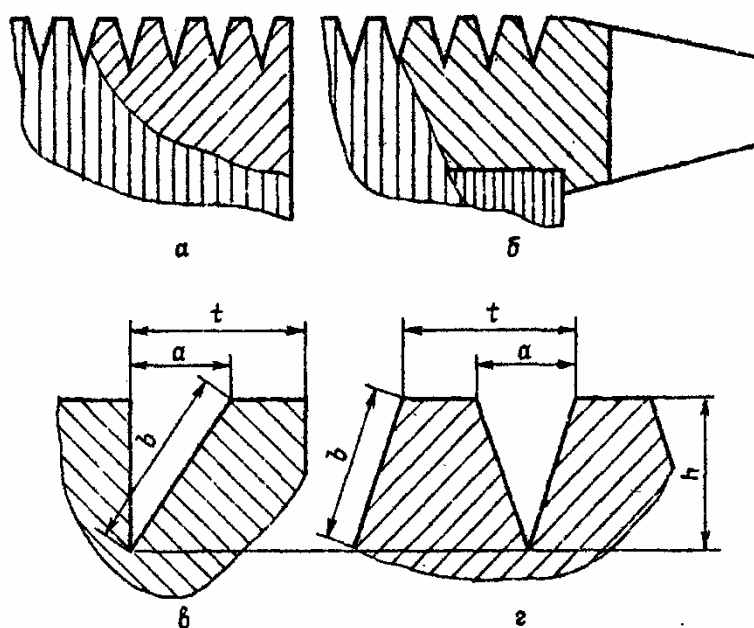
Форма гвинтової канавки на поверхні ротора
